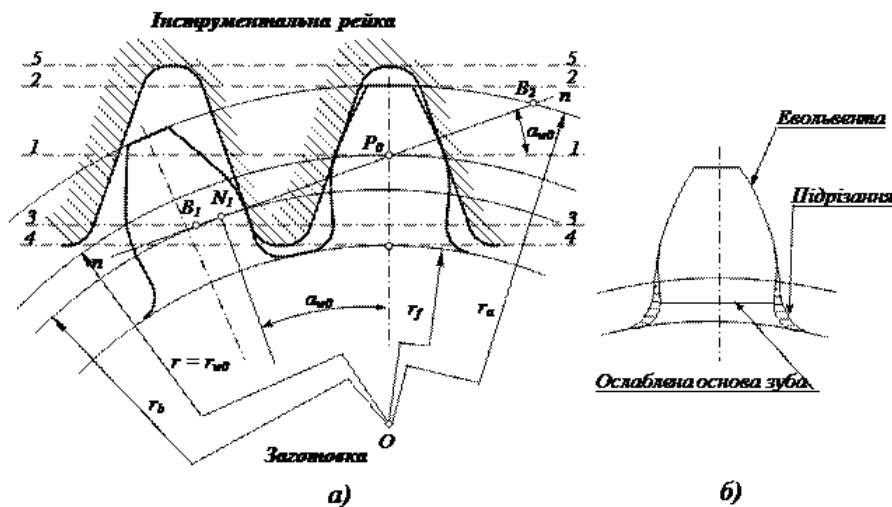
До питання підрізання зубців при виготовленні зубчастих коліс
